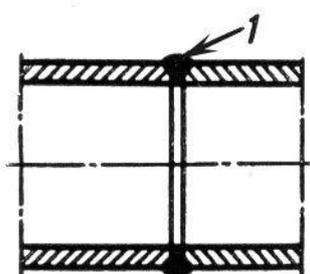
Сварное соединение: 1 – сварной шов
